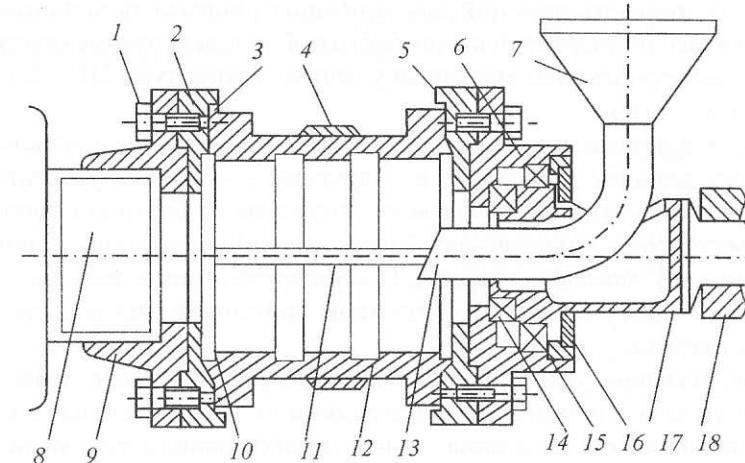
Пристрій для заливки вкладишів підшипників:
